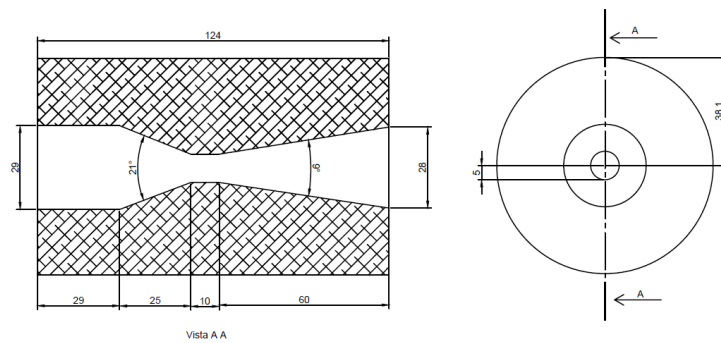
Desenho do Tubo Venturi usinado adotado no equipamento de teste desenvolvido.
